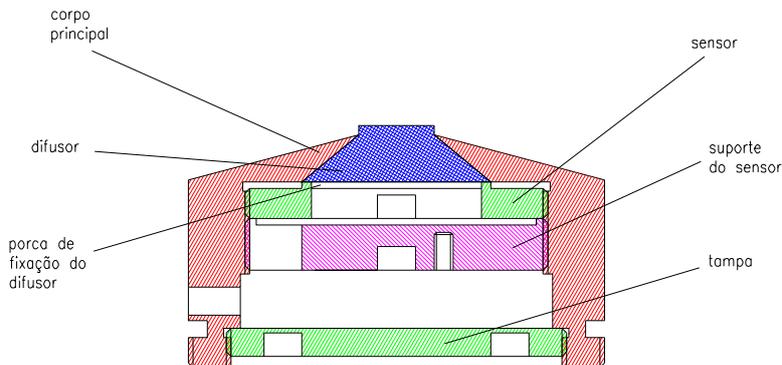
Desenho ilustrativo do corpo principal do radiômetro
